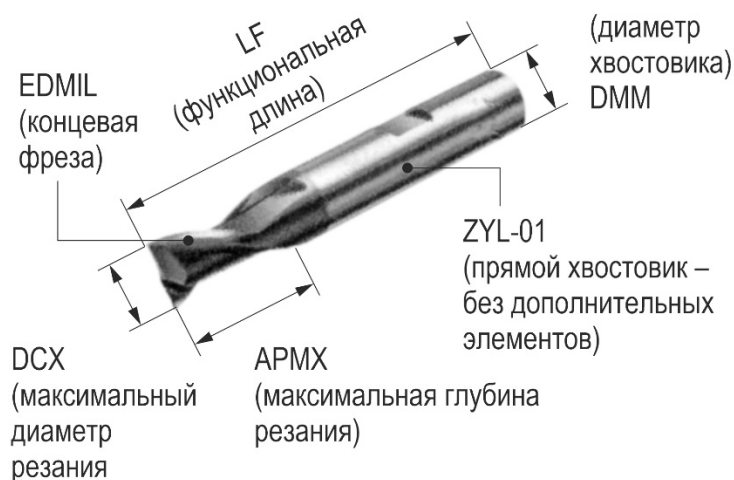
Пример стандартных обозначения параметров концевой фрезы
